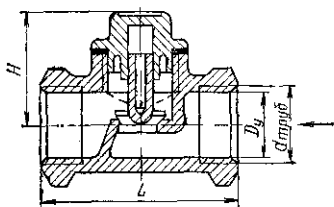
Клапан обратный подъемный муфтовый 16Б1бк
